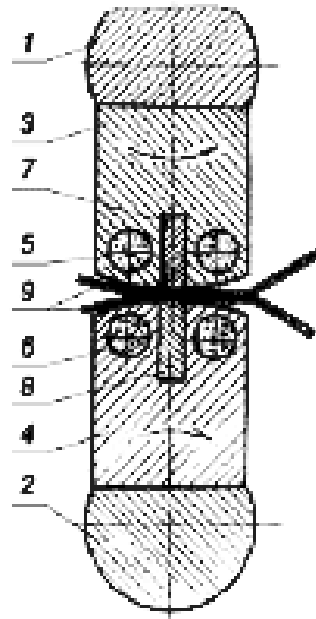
Губки теплового зварювання, які розміщені на роторах. 1, 2 – роторні вали; 3 – верхня губка; 4 – нижня губка; 5, 6 – нагрівачі плівки; 7 – нерухомий ніж; 8 – твердосплавна пластина; 9 – матеріал пакувальний.
